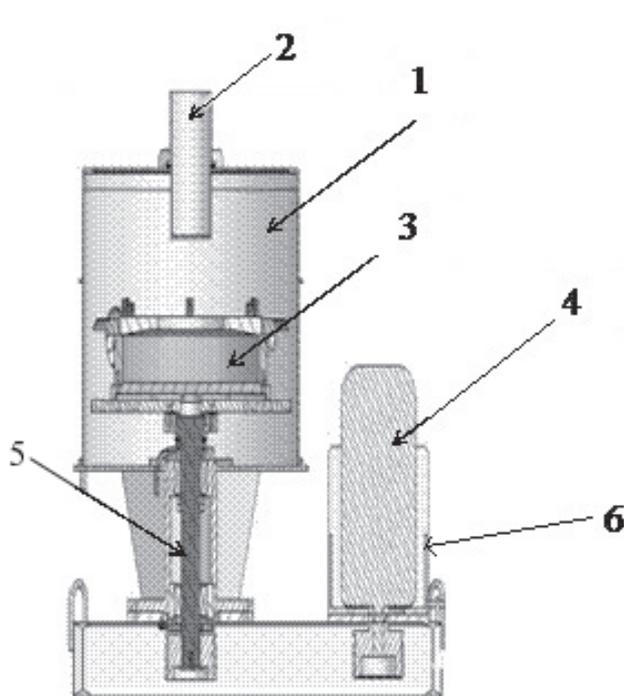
Принципиальная схема установки центробежного литья: 1 — защитный кожух; 2 — заливная горловина; 3 — кристаллизатор; 4 — двигатель; 5 — привод; 6 — станина
